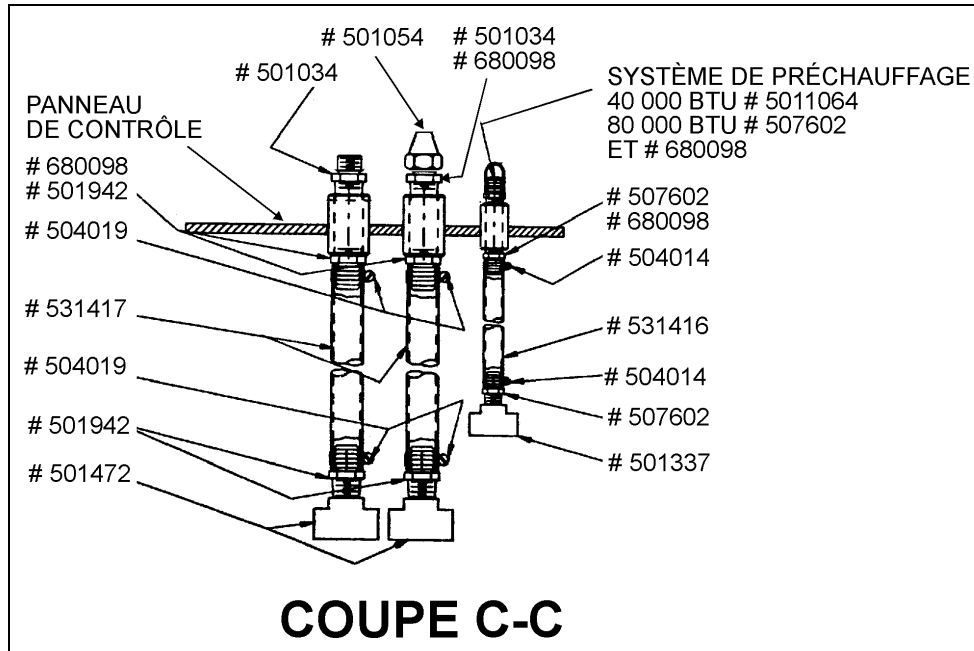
ASSEMBLAGE DES TUBES DE SUCCION
